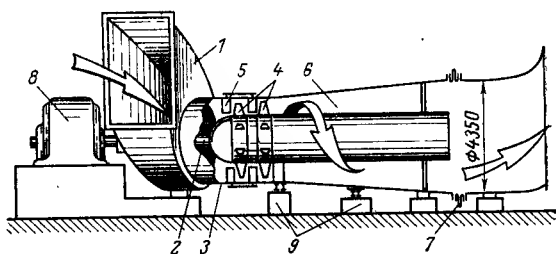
Устройство дымососа осевого типа. 1 — всасывающий патрубок; 2 — вал; 3 — корпус; 4 — рабочее колесо с лопатками; 5 — направляющий аппарат; 6 — диффузор; 7 — компенсатор; 8 — электродвигатель; 9 — опоры.
